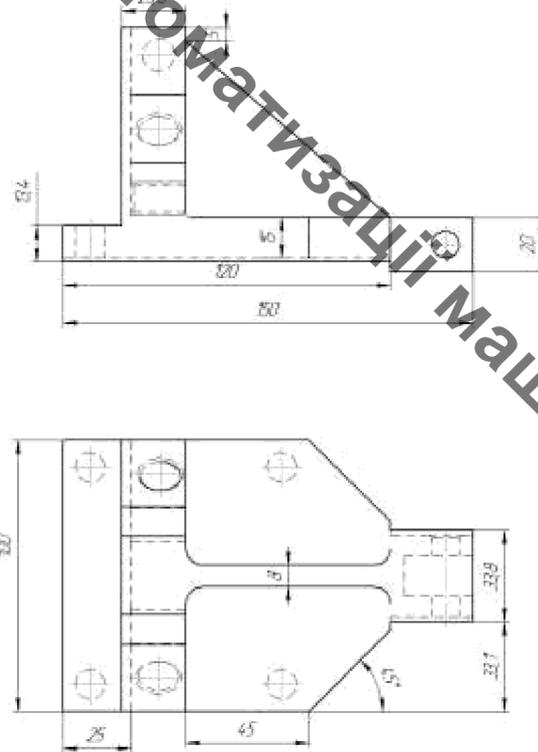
Ескіз заготовки в піщано-глинисті форми
